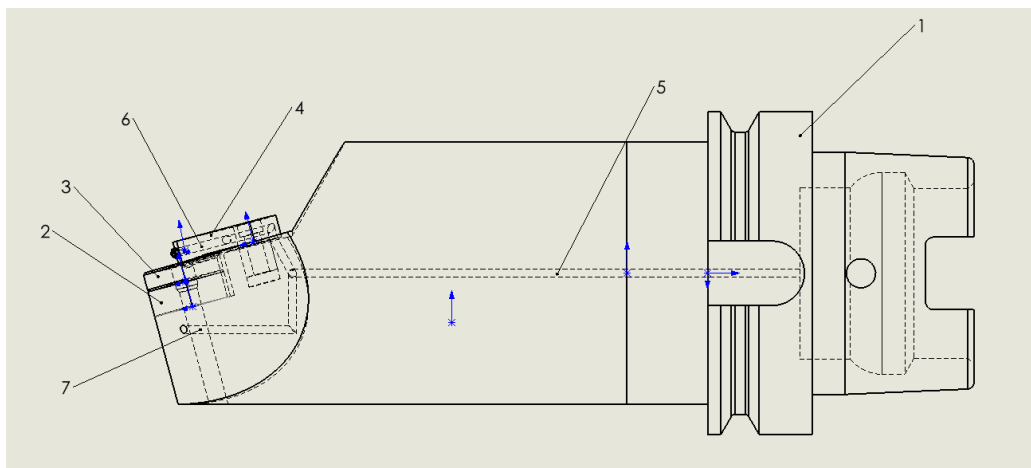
Вид справа резца с державкой HSK и внутренним подводом СОЖ через крепление пластинки.
